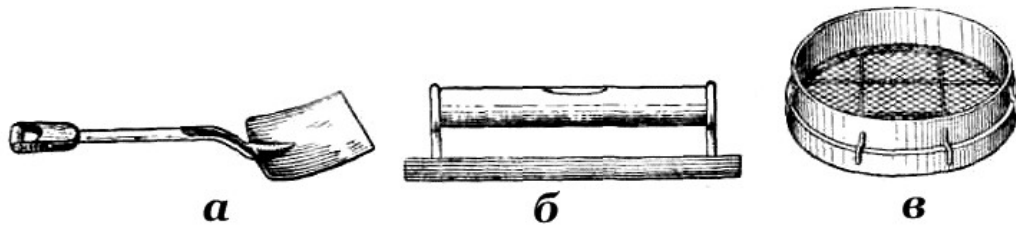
Формовочный и отделочный инструмент: а – лопата; б – ва-терпас; в – сито
